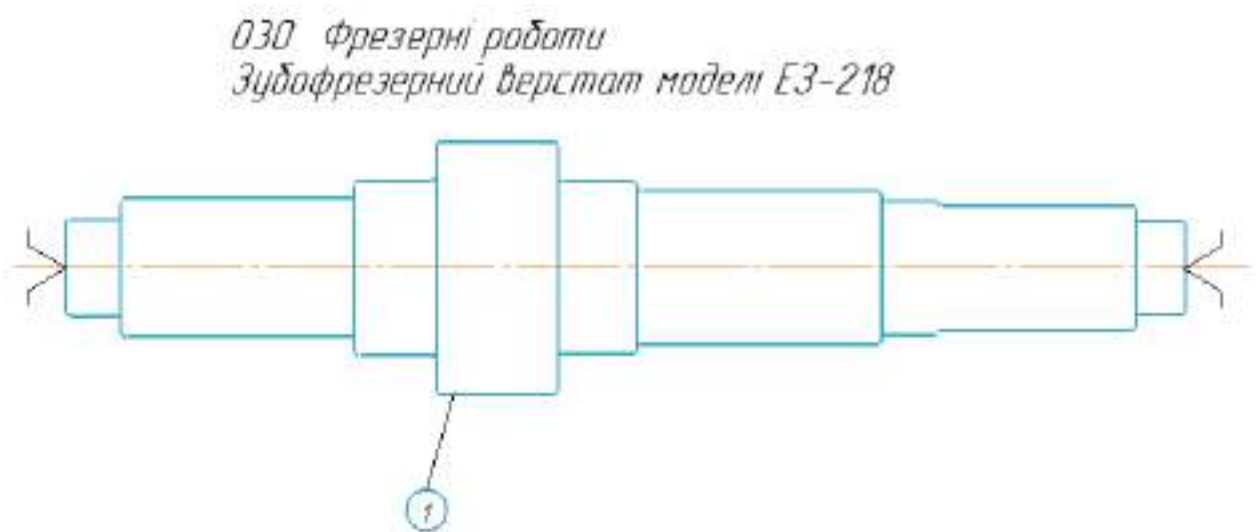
Карта ескізів «Фрезерні роботи»
